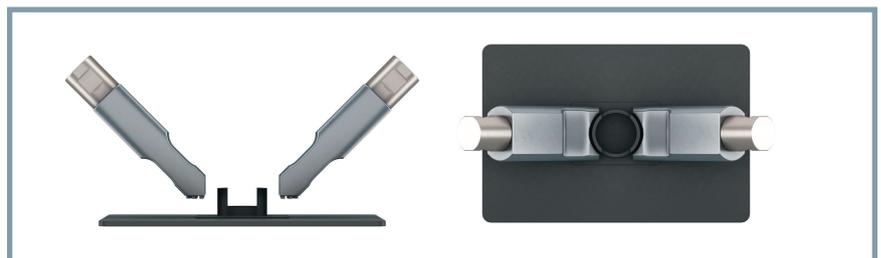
Prinzip des 45°-Verschweißens. Dabei kommen sogenannte „Sichel-Sonotroden“ zum Einsatz © Magna Exteriors
